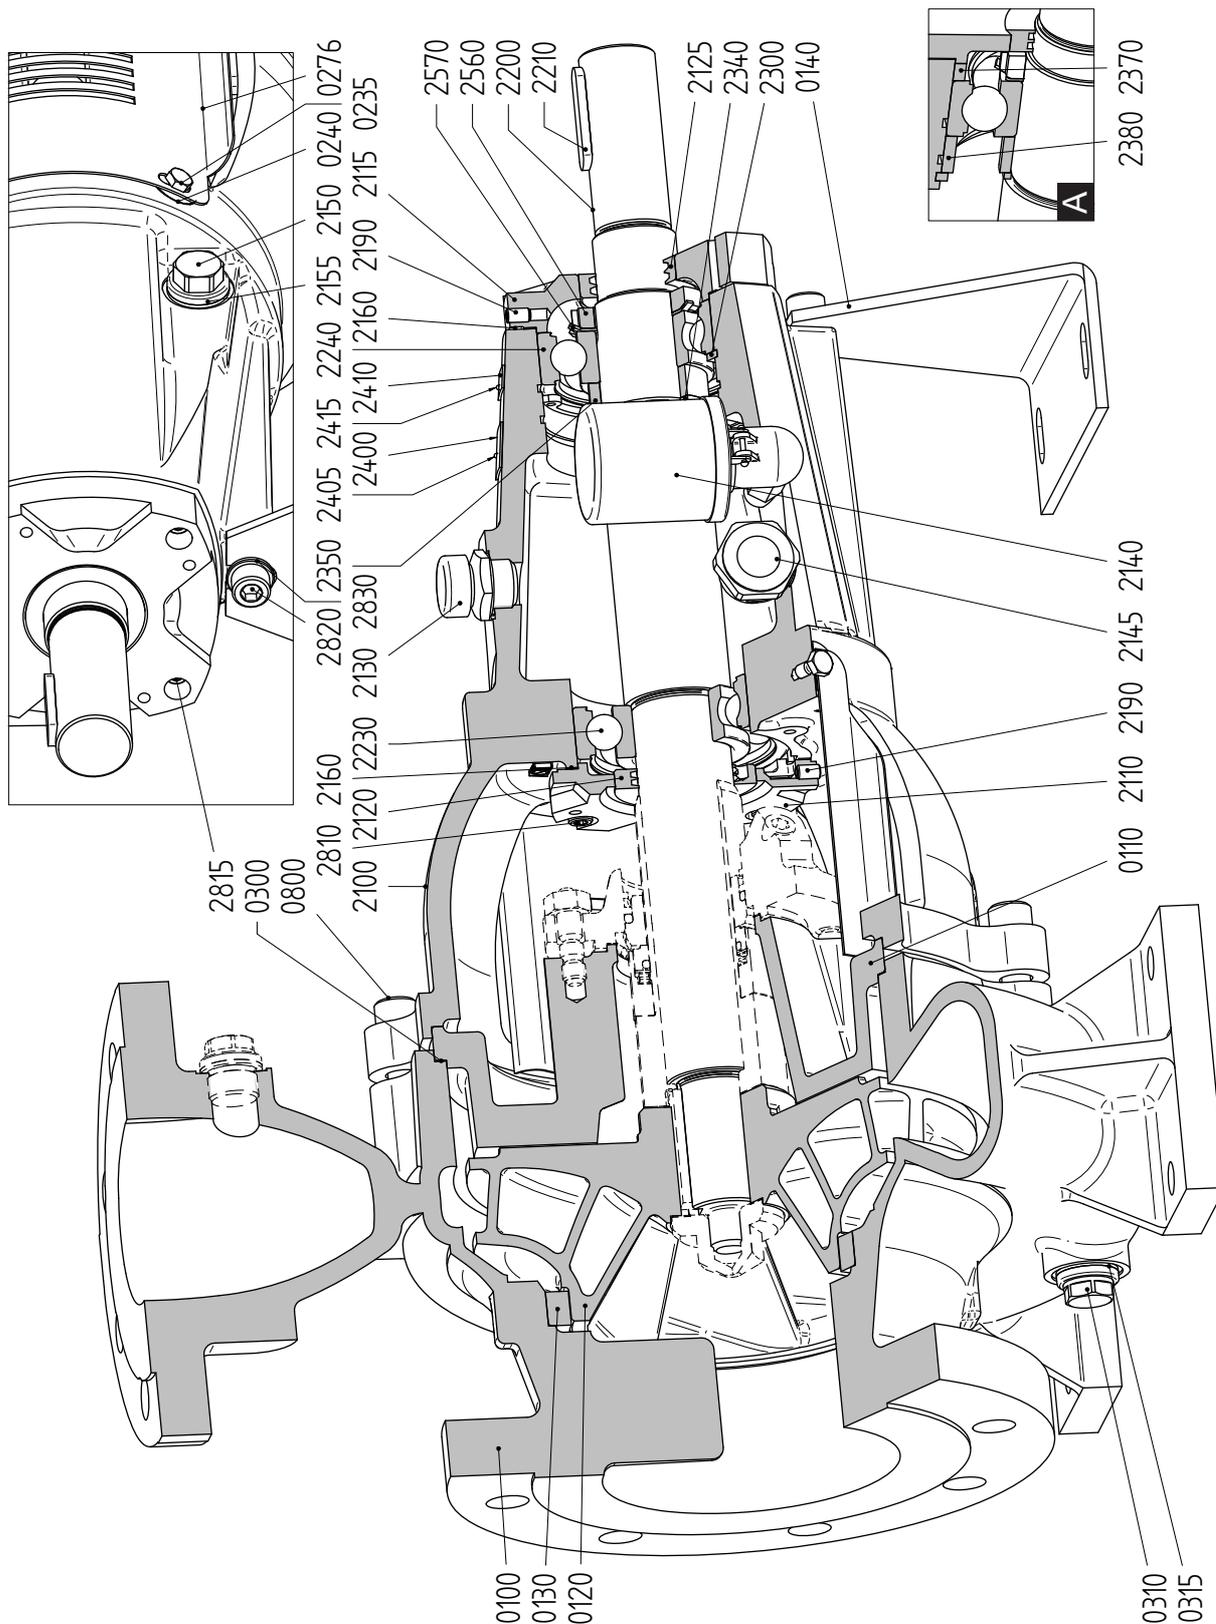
Чертеж в разрезе L3 с коническим отверстием (A = для группы подшипников 3)
